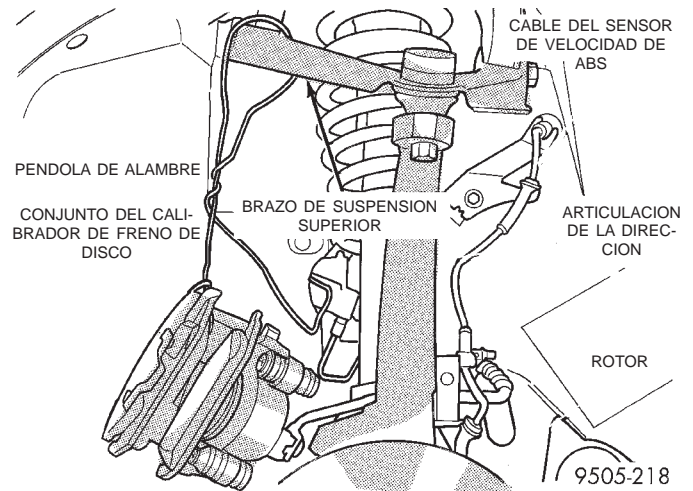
Montaje del calibrador de freno de disco delantero
